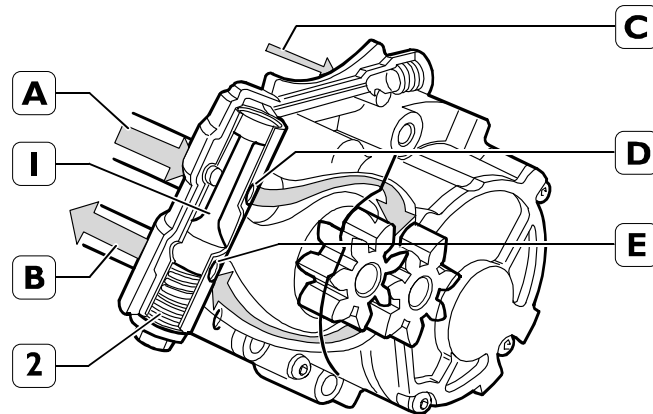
Vista em perspectiva do grupo bomba de óleo depressor
